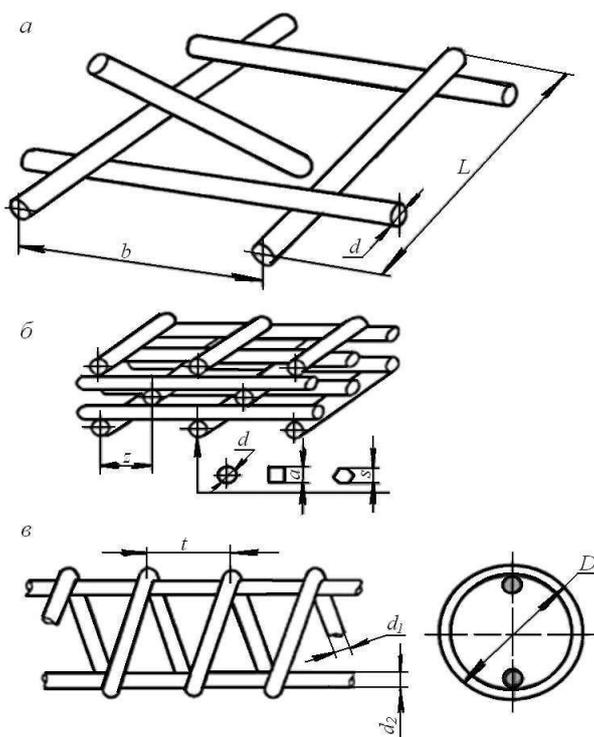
Размеры и форма внутренних холодильников [3 с. 209]: а – ежей; б – сварных решеток; в – спиралей
